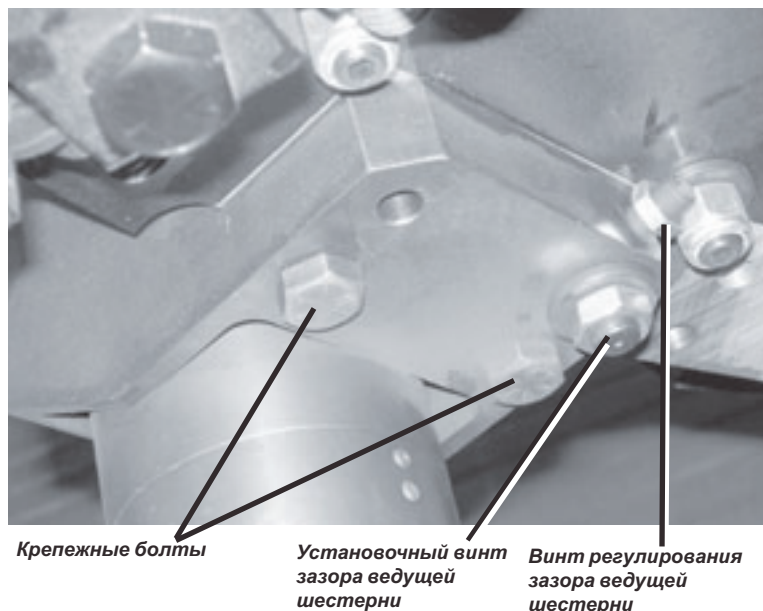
Два болта фиксируют крепление пневматического двигателя к раме. Для выставления зазора ведущей шестерни следует отвернуть установочный винт и поворачивать регулировочный винт. Затяните установочный винт.
